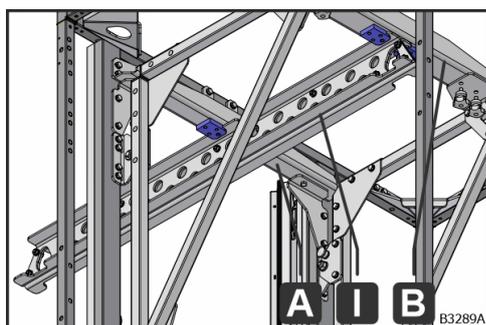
Insertion du bras porteur (I) dans la plaque de guidage arrière
